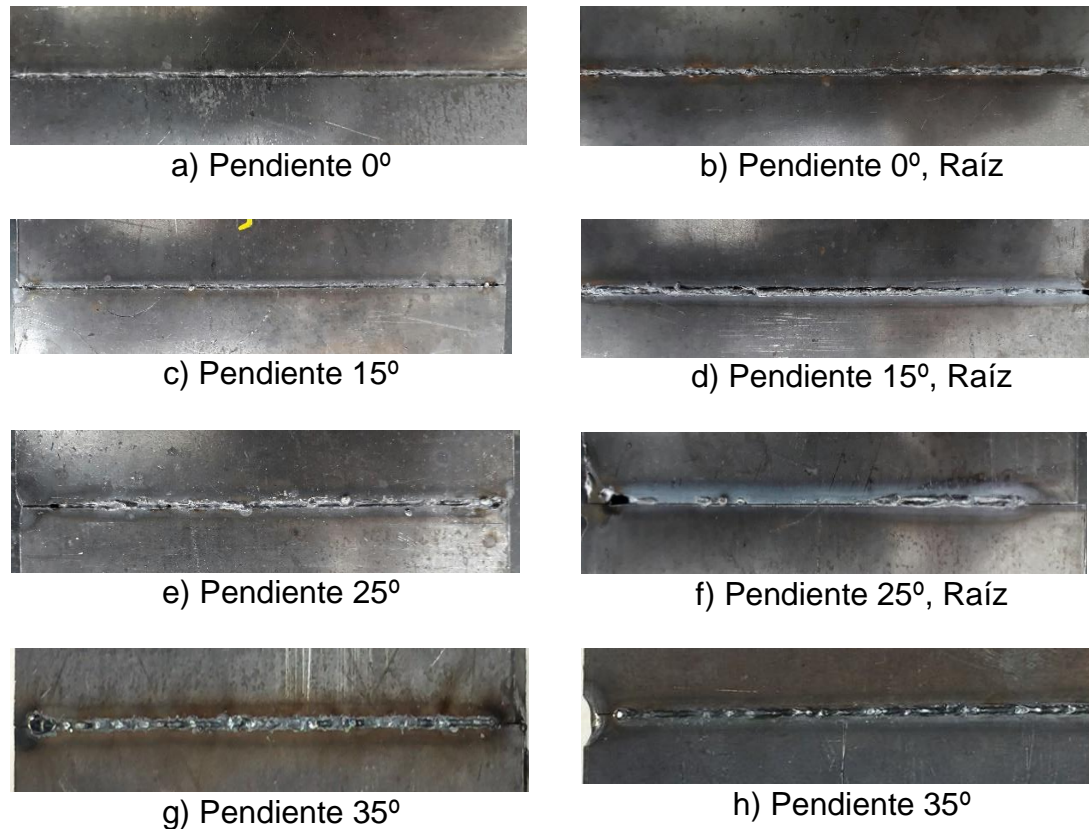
11. Superficie de la soldadura LBW,
